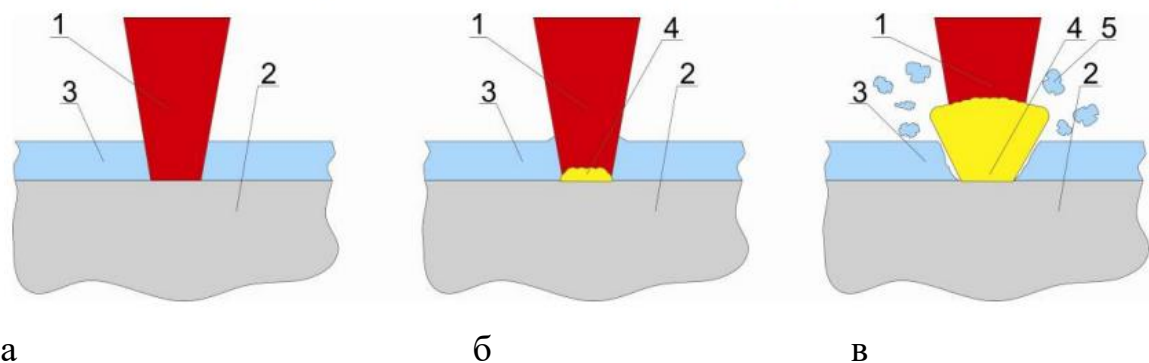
Випарний механізм лазерного очищення при проходженні лазерного імпульсу крізь забруднену поверхню до металу (а), при розігріванні металу (б) і безпосередньо процес випарювання металу (в)
